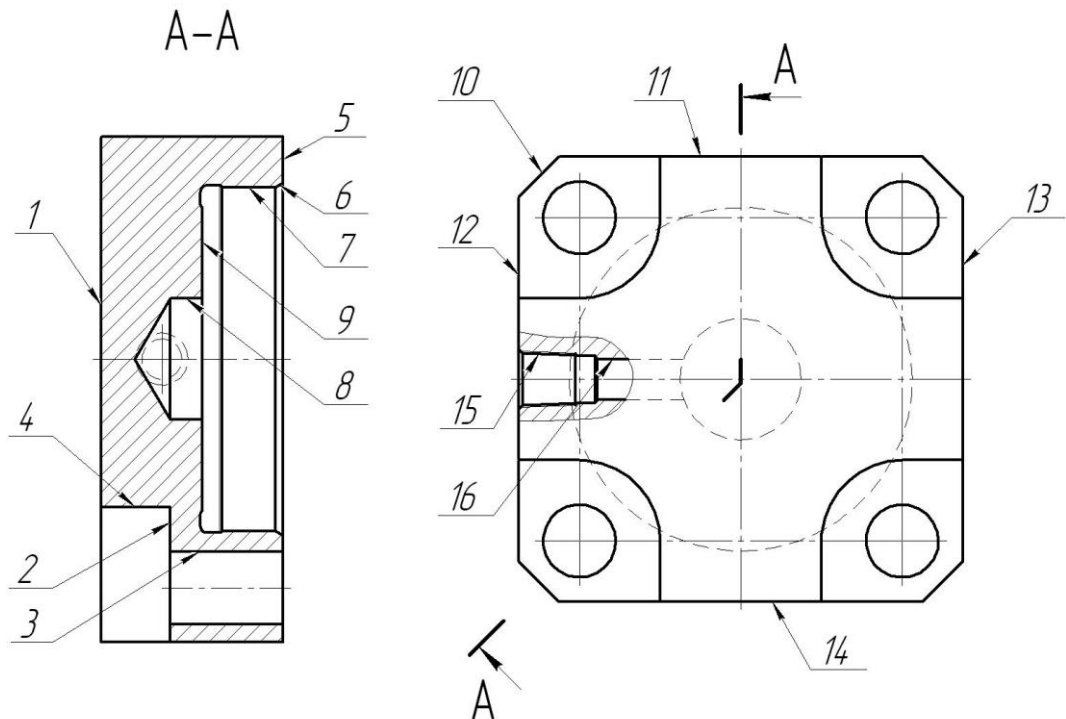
Оброблювані поверхні деталі «Фланець»
